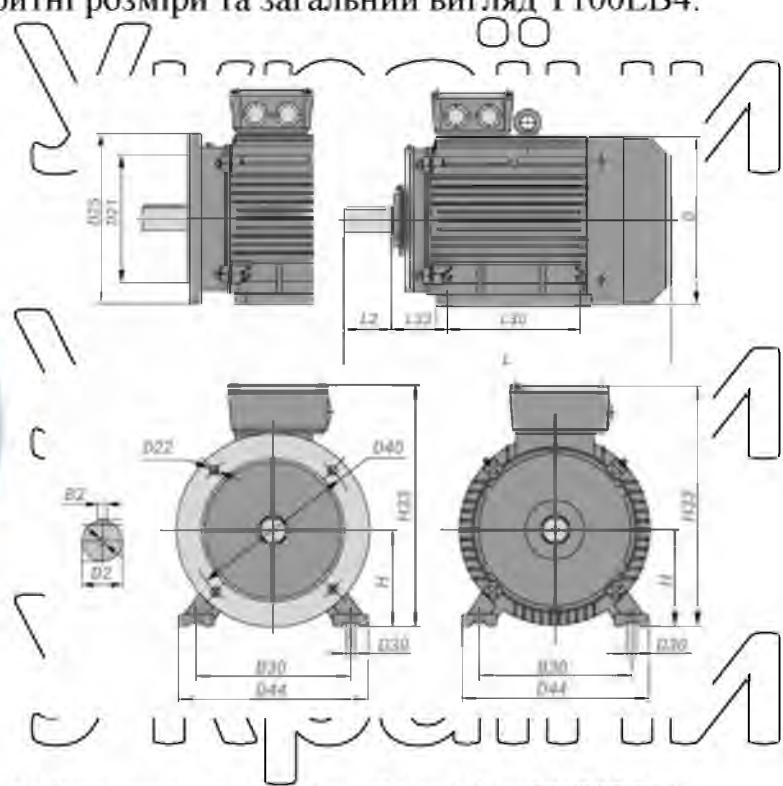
Загальний вигляд та габаритні розміри T100LB4.
